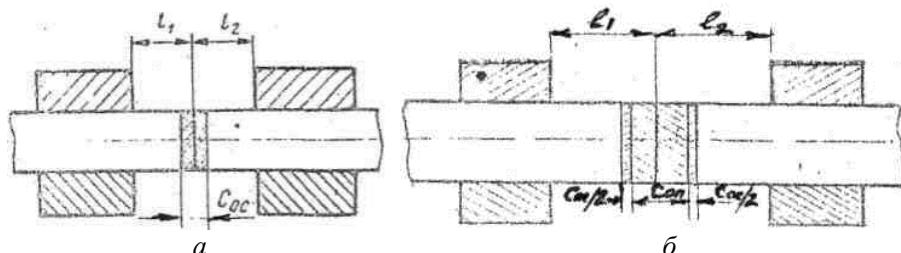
Схема установки свариваемых деталей при стыковой сварке:
